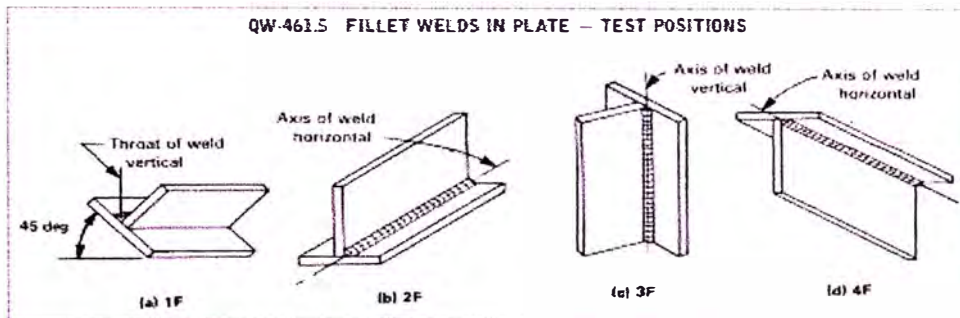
posiciones de prueba en planchas – Juntas de Filete
